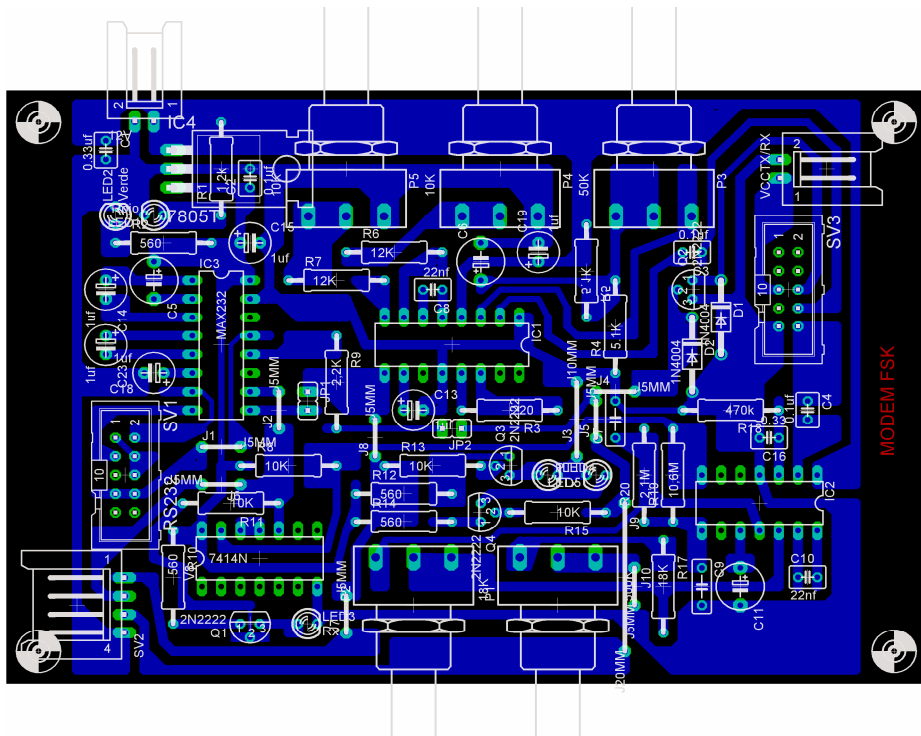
Vista de Componentes Tarjeta MODEM FSK
